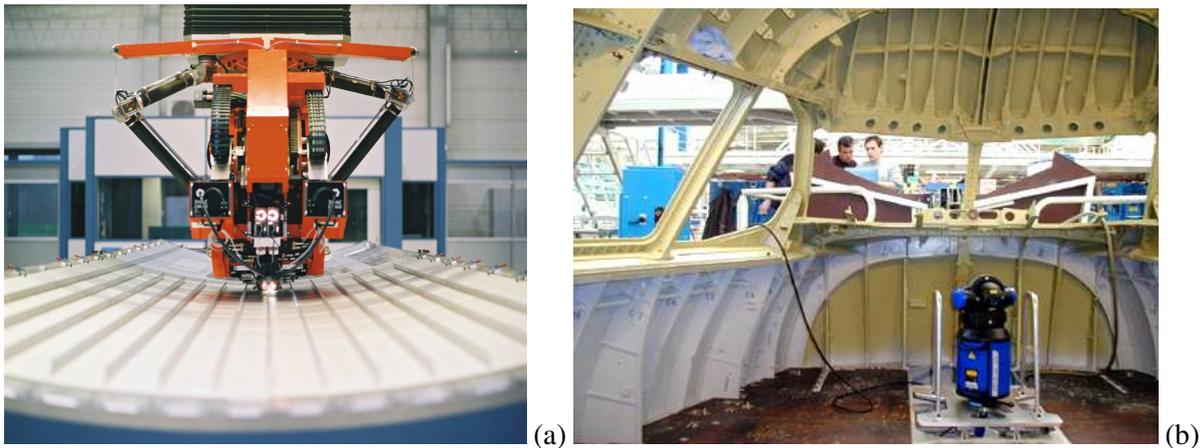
Processos laser na fábrica da Airbus: (a) soldagem e (b) posicionamento.
